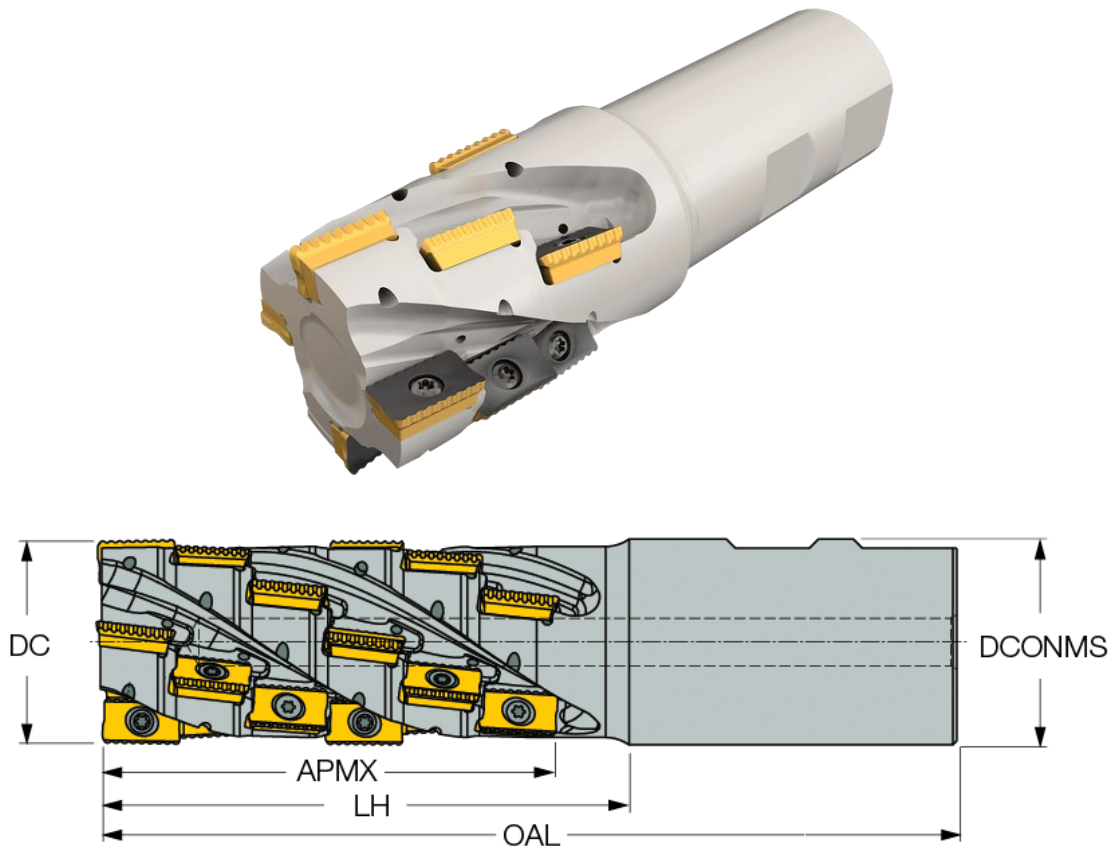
Фреза P290 ACK D40-3-53-W32-18
